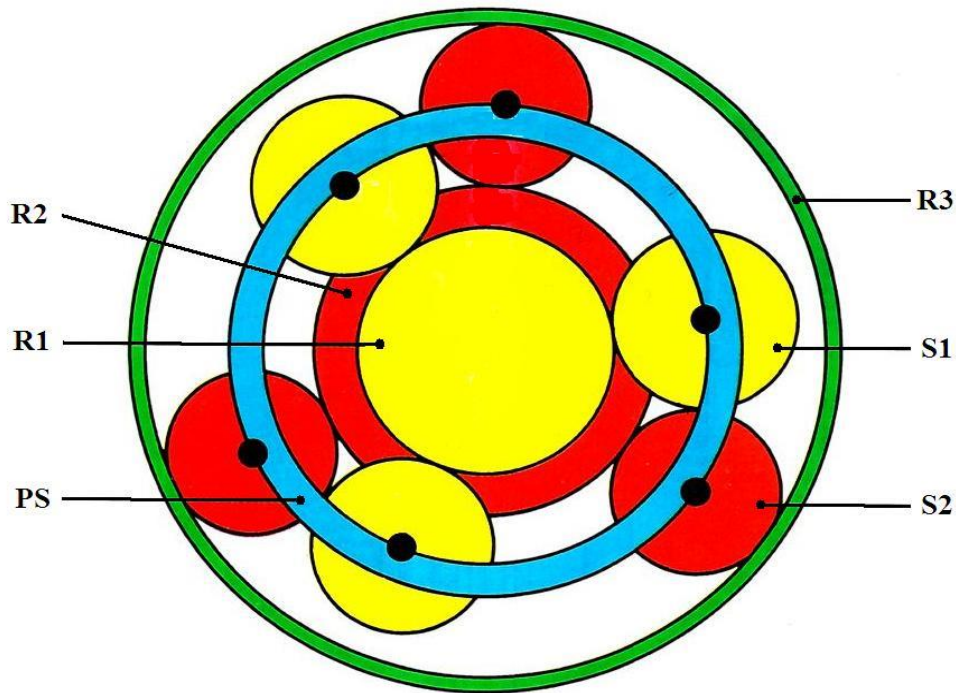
Sistem de roți planetare „Ravigneaux”
